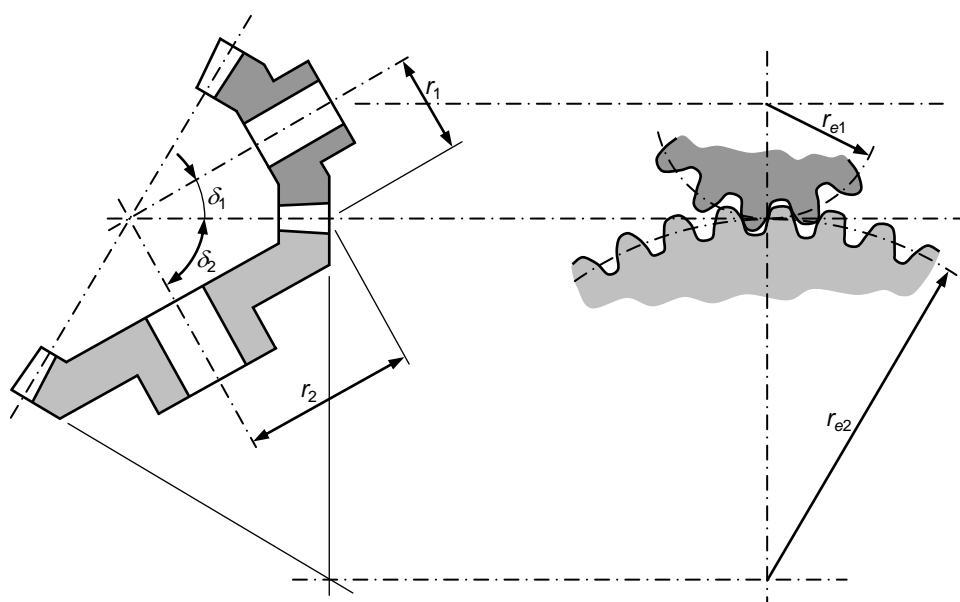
Engrenagem cônica e engrenagem cilíndrica equivalente.
